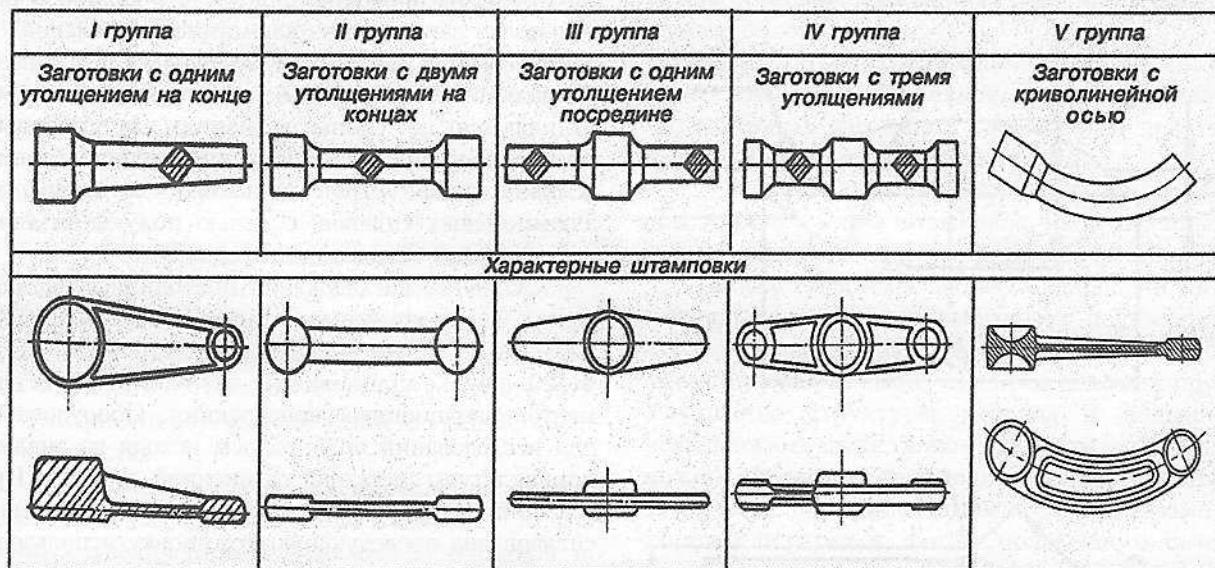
Классификация типовых представителей заготовок, валыцаемых на ковочных вальцах
